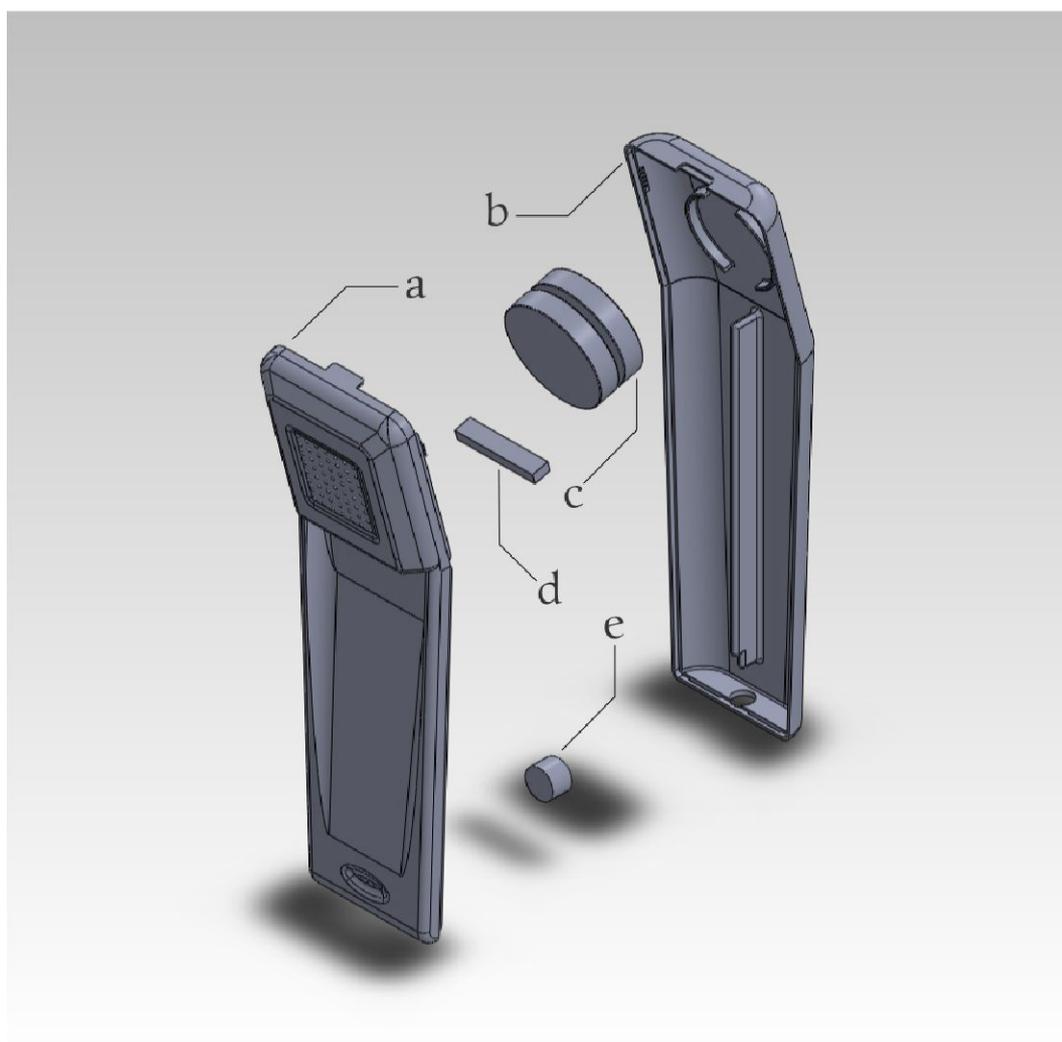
Fone do CHU 2836. Perspectiva explodida.
